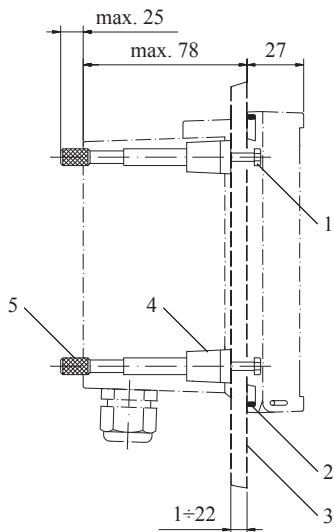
zestaw do montażu rurowego (Wszystkie wymiary podane zostały w mm)
